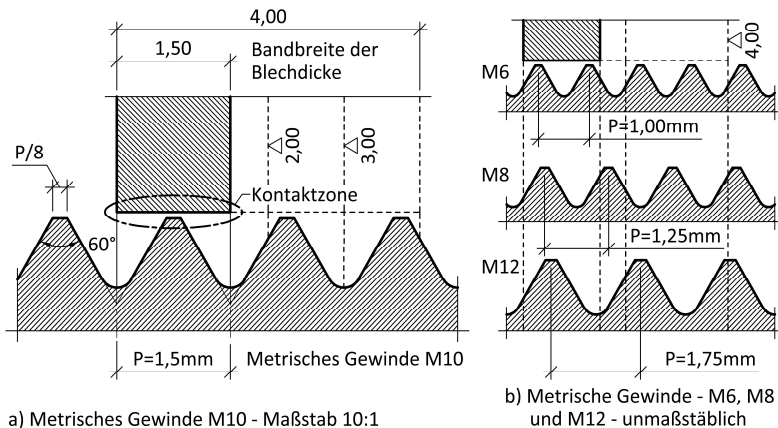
Gewindegeometrien und Blechdicken für die untersuchten Konfigurationen
